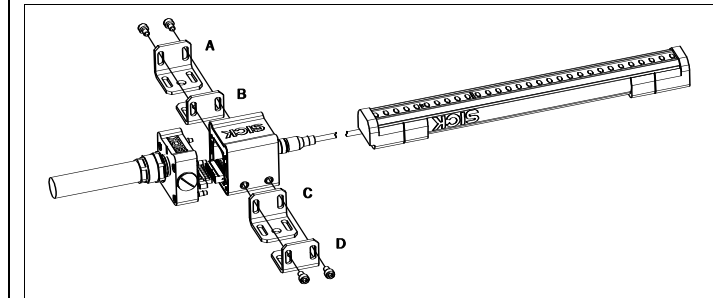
Montagevarianten Befestigungswinkel für Adapter FGS/deTec4 (A bis D)
